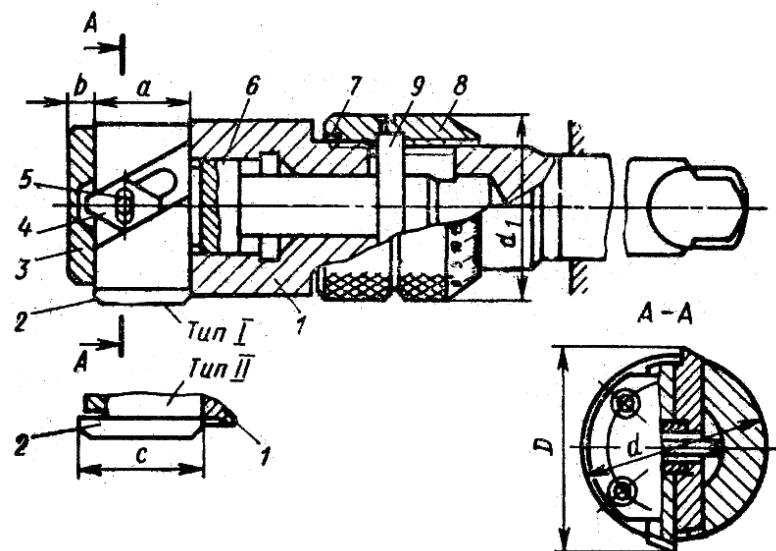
Дволезова розвертка з мікрометричним регулювальним пристроєм
